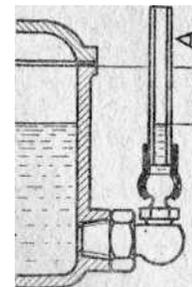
; Приспособление для измерений уровня топлива в поплавковой камере»
